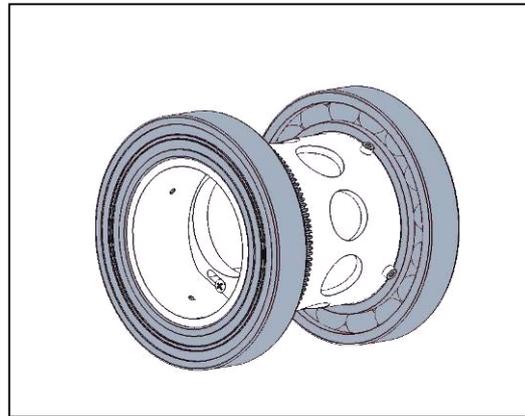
An den Enden des Zylinders sind zwei Kugellager (grau) aufgepresst, deren Position am Zylinder durch Inbusschrauben markiert ist.
